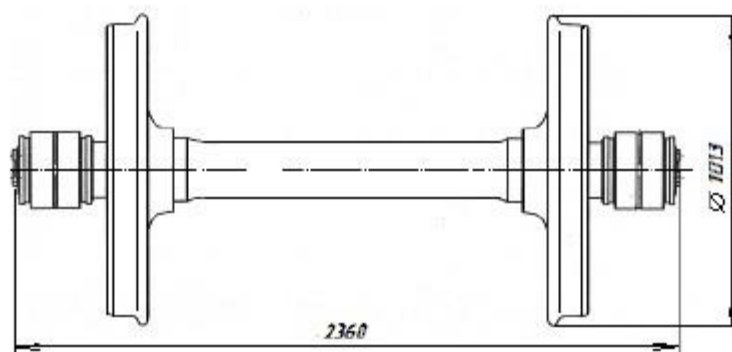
Колесные пары типа РУ1Ш-957-Г и РВ2Ш-957-Г с подшипниками под адаптер. Габаритные размеры
